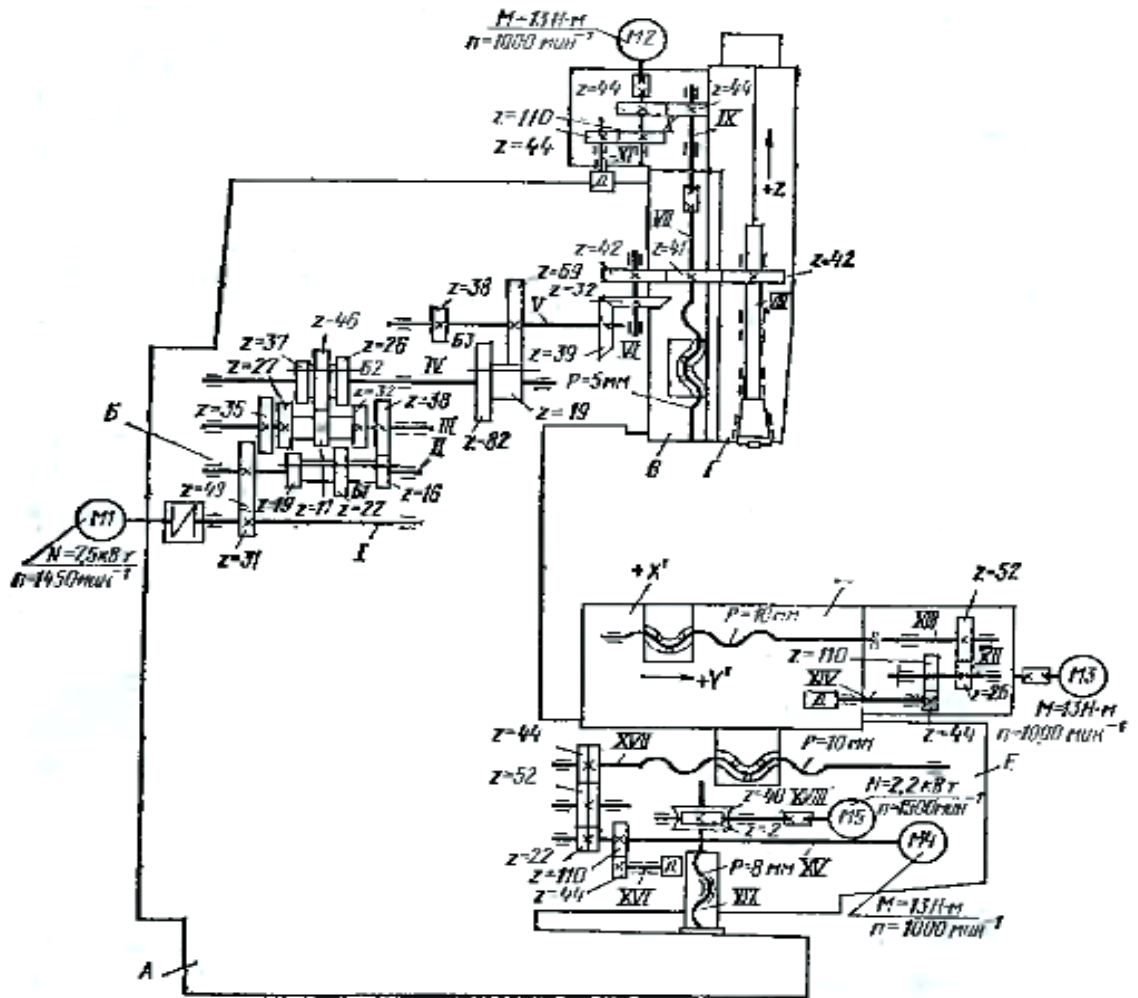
Кінематична схема вертикально-фрезерного верстата 6Р13Ф3 з ЧПК
